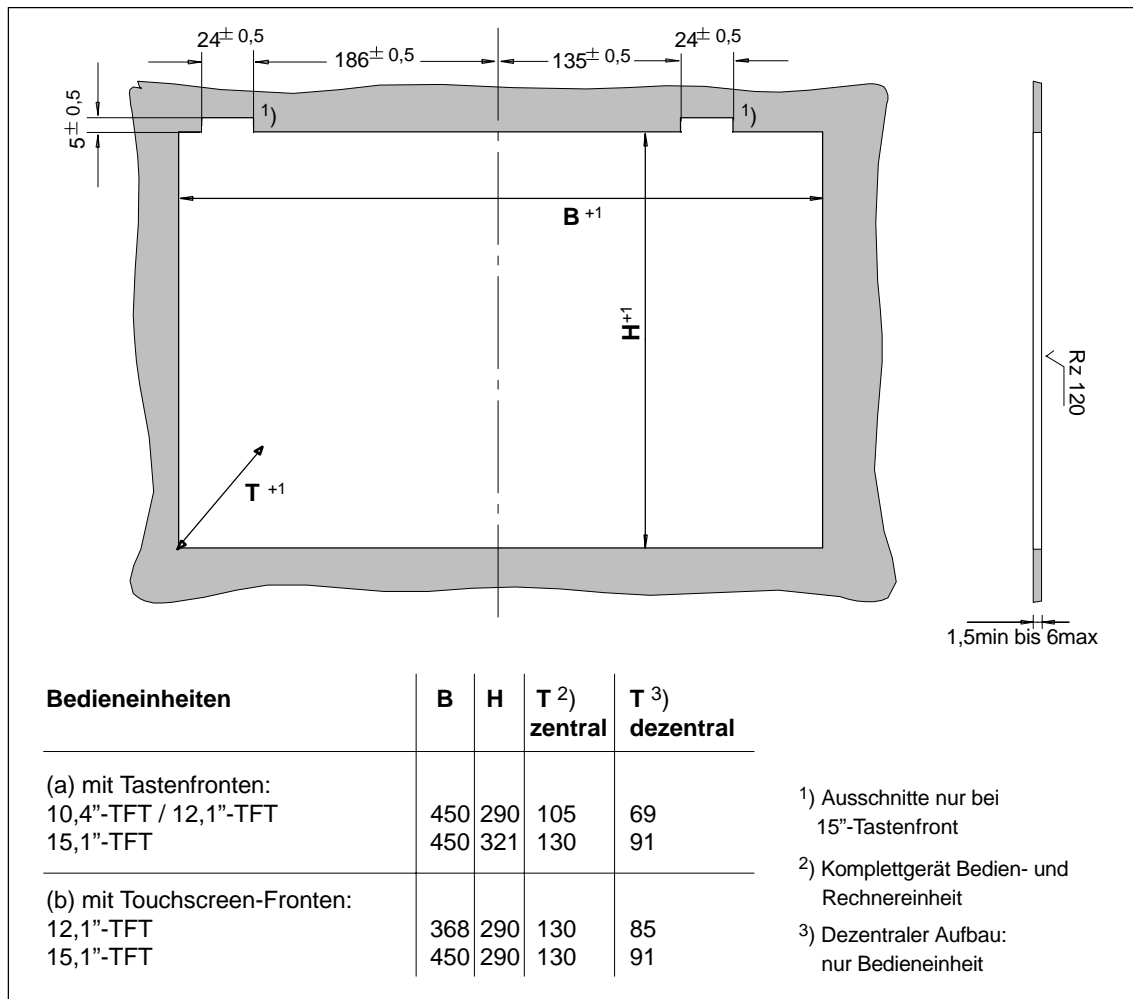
Einbauausschnitt für Standardeinbau Panel PC 670 (Angaben: Breite x Höhe x Tiefe in mm)
